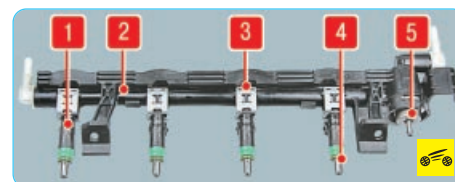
Топливная рампа: 1 – форсунка; 2 – рампа; 3 – фиксатор форсунки; 4 – уплотнительное кольцо форсунки; 5 – регулятор давления топлива
